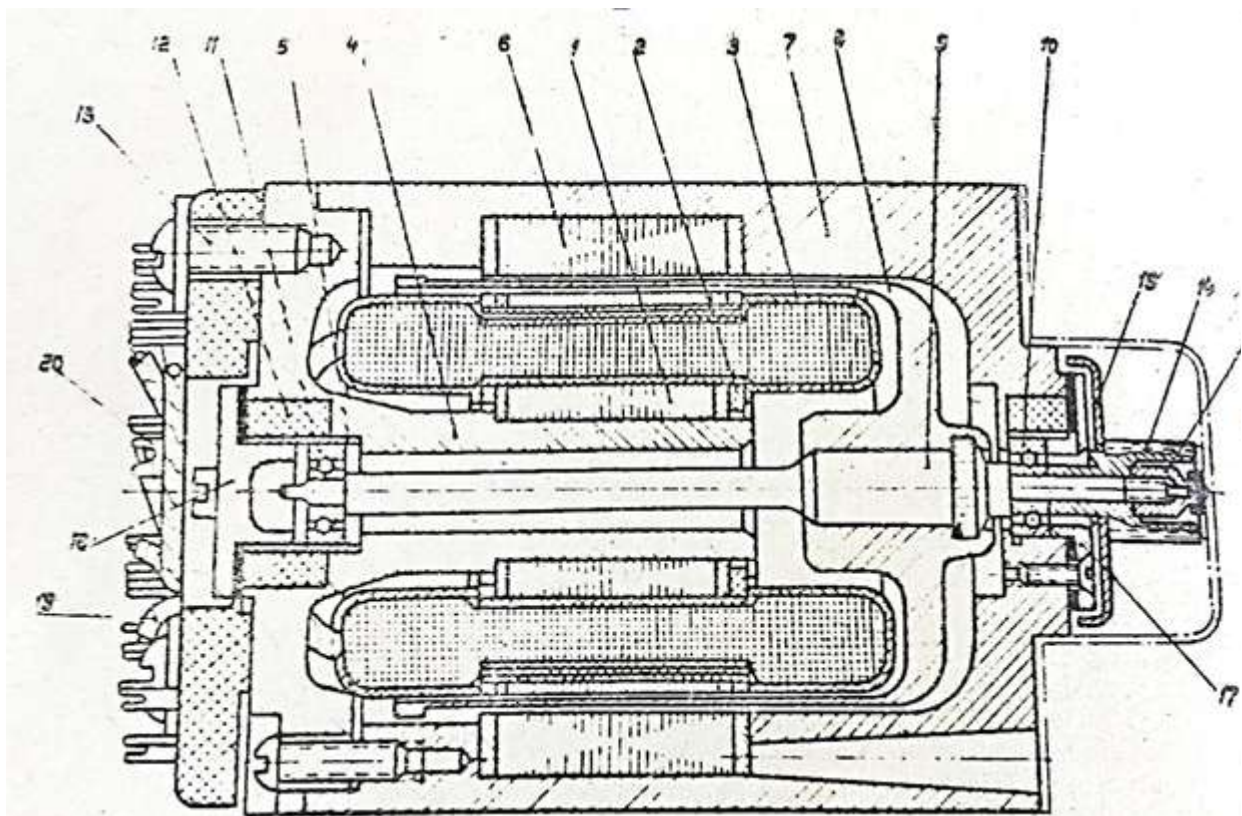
Конструкция ДИД: 1 – пакет статора; 2 – изоляционная пластина; 3 – колпачок; 4 – сердечник; 5 – стальная втулка; 6 – наружный магнитопровод; 7 – корпус; 8 – ротор; 9 – вал; 10 – передний подшипник; 11 – задний подшипник; 12 – сальник; 13 – винт; 14 – трубка; 15 – экран; 16 – гайка; 17 – передняя крышка; 18 – задняя крышка; 19 – ламели; 20 – панель
